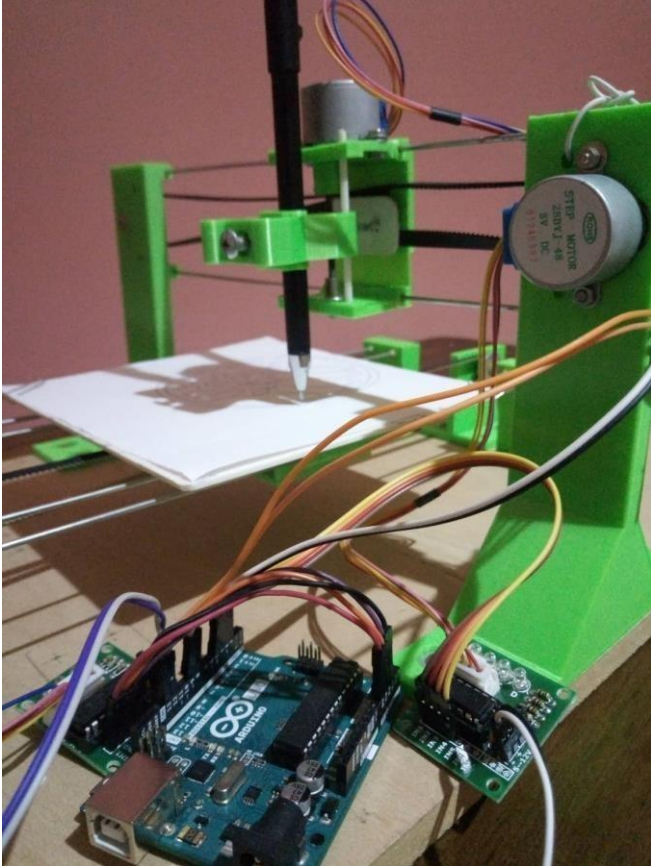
Photo d'assemblage de la partie électronique de l'imprimante CNC.
